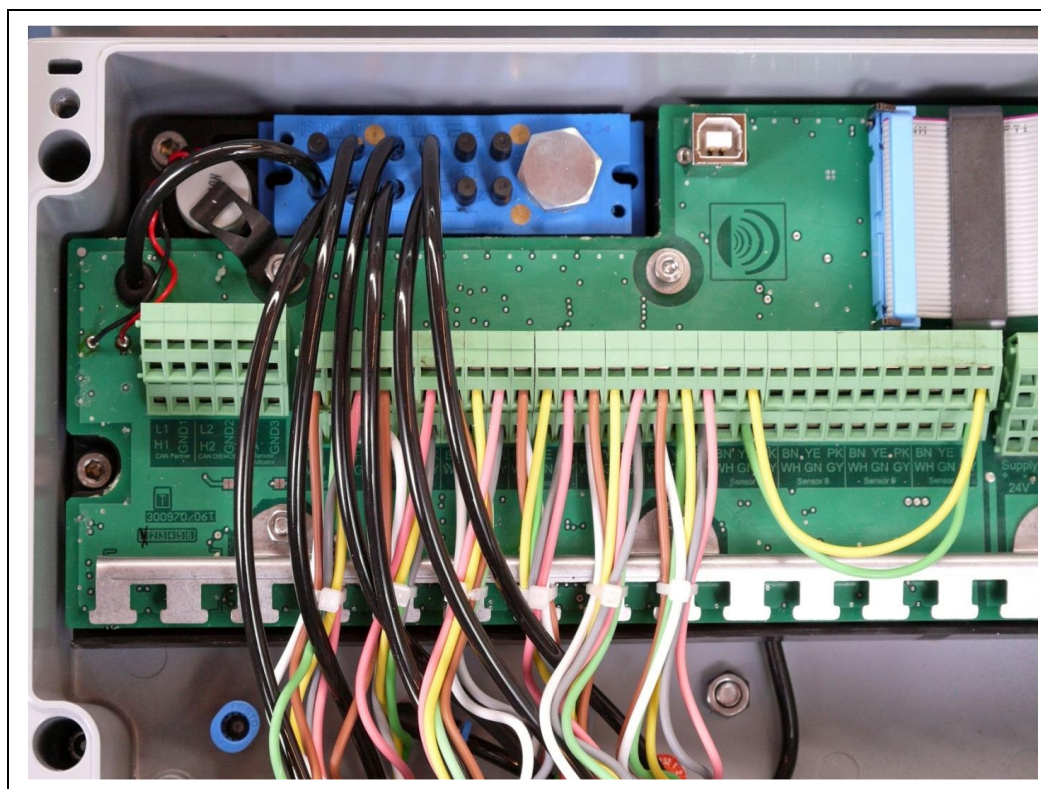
Montaggio e installazione terminati (passaggi 1 - 7; ad es. con 6 flessibili ibridi)
